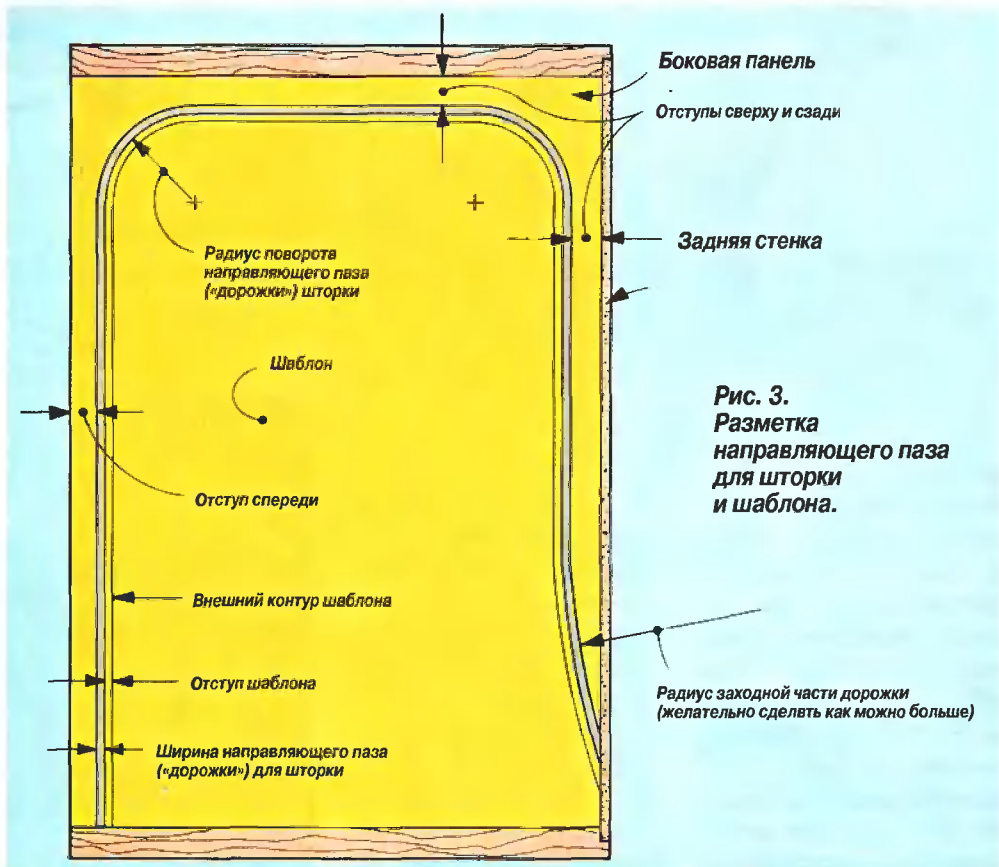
Разметка направляющего паза для шторки и шаблона.
